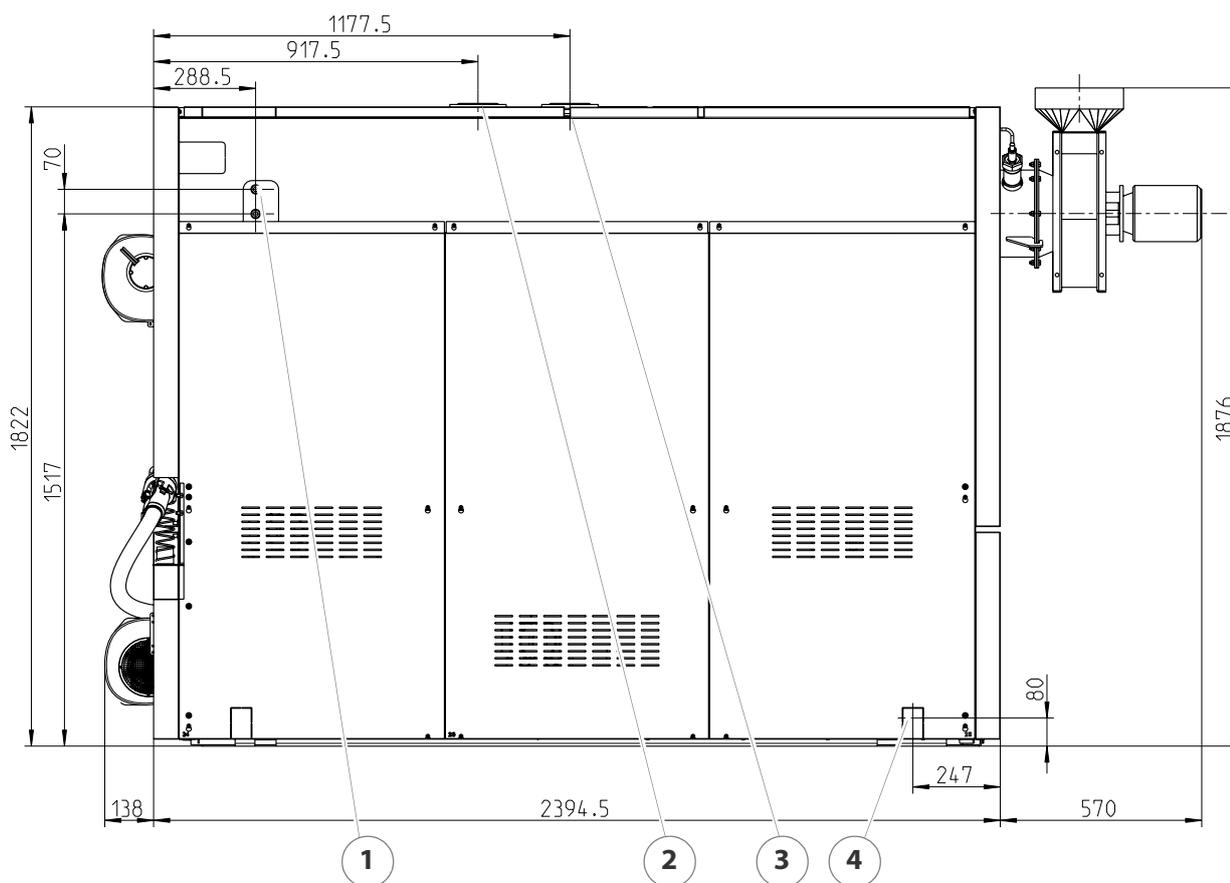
/1 - Dimensions à l'arrière HDG M175 - 240 (sans filtre)
